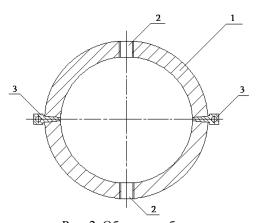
Образец в сборе. 1- образец; 2- отверстие для закрепления образца; 3- штифт.
